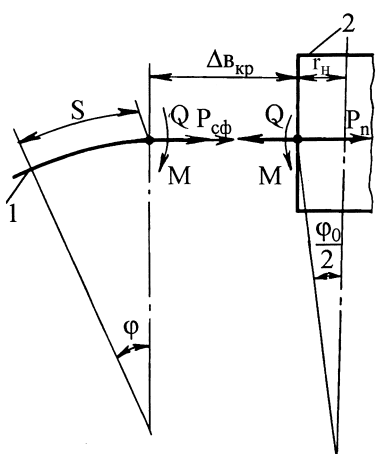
Расчетная схема конструкции: 1 — сферическая оболочка; 2 — цилиндрический патрубок; s, φ — текущие значения дуговой координаты и соответствующего центрального угла
